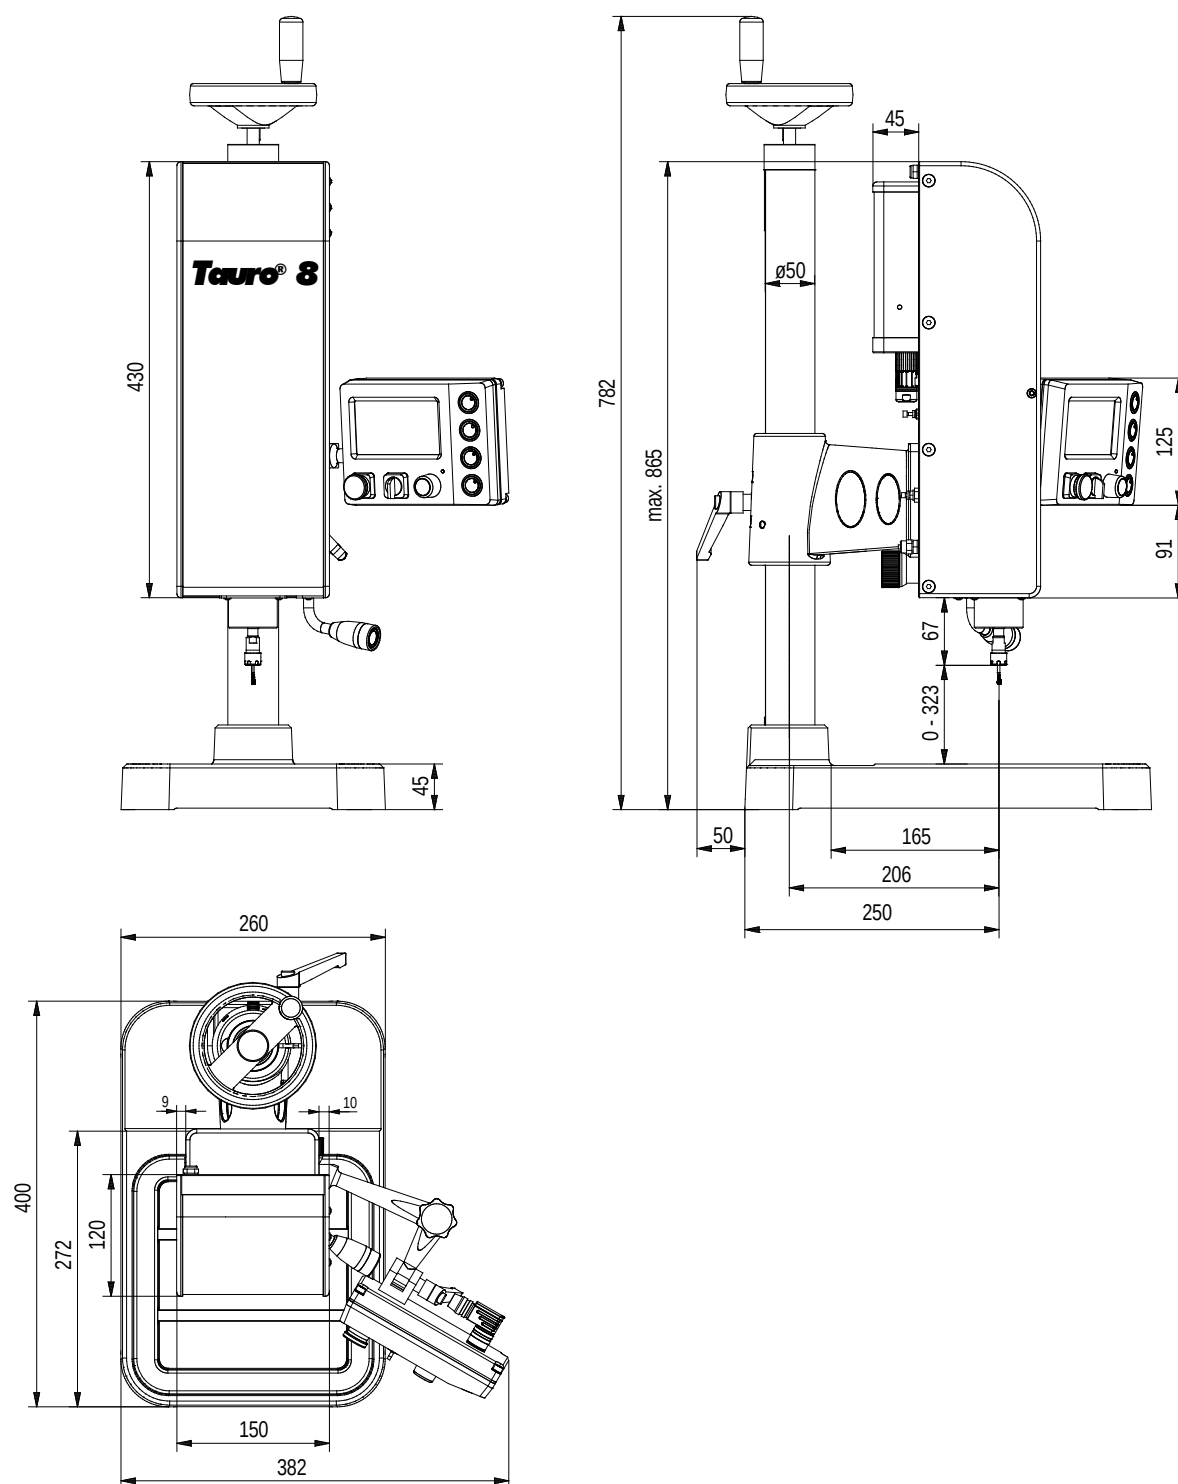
Vues de la machine à usiner les filets Tauro 8
